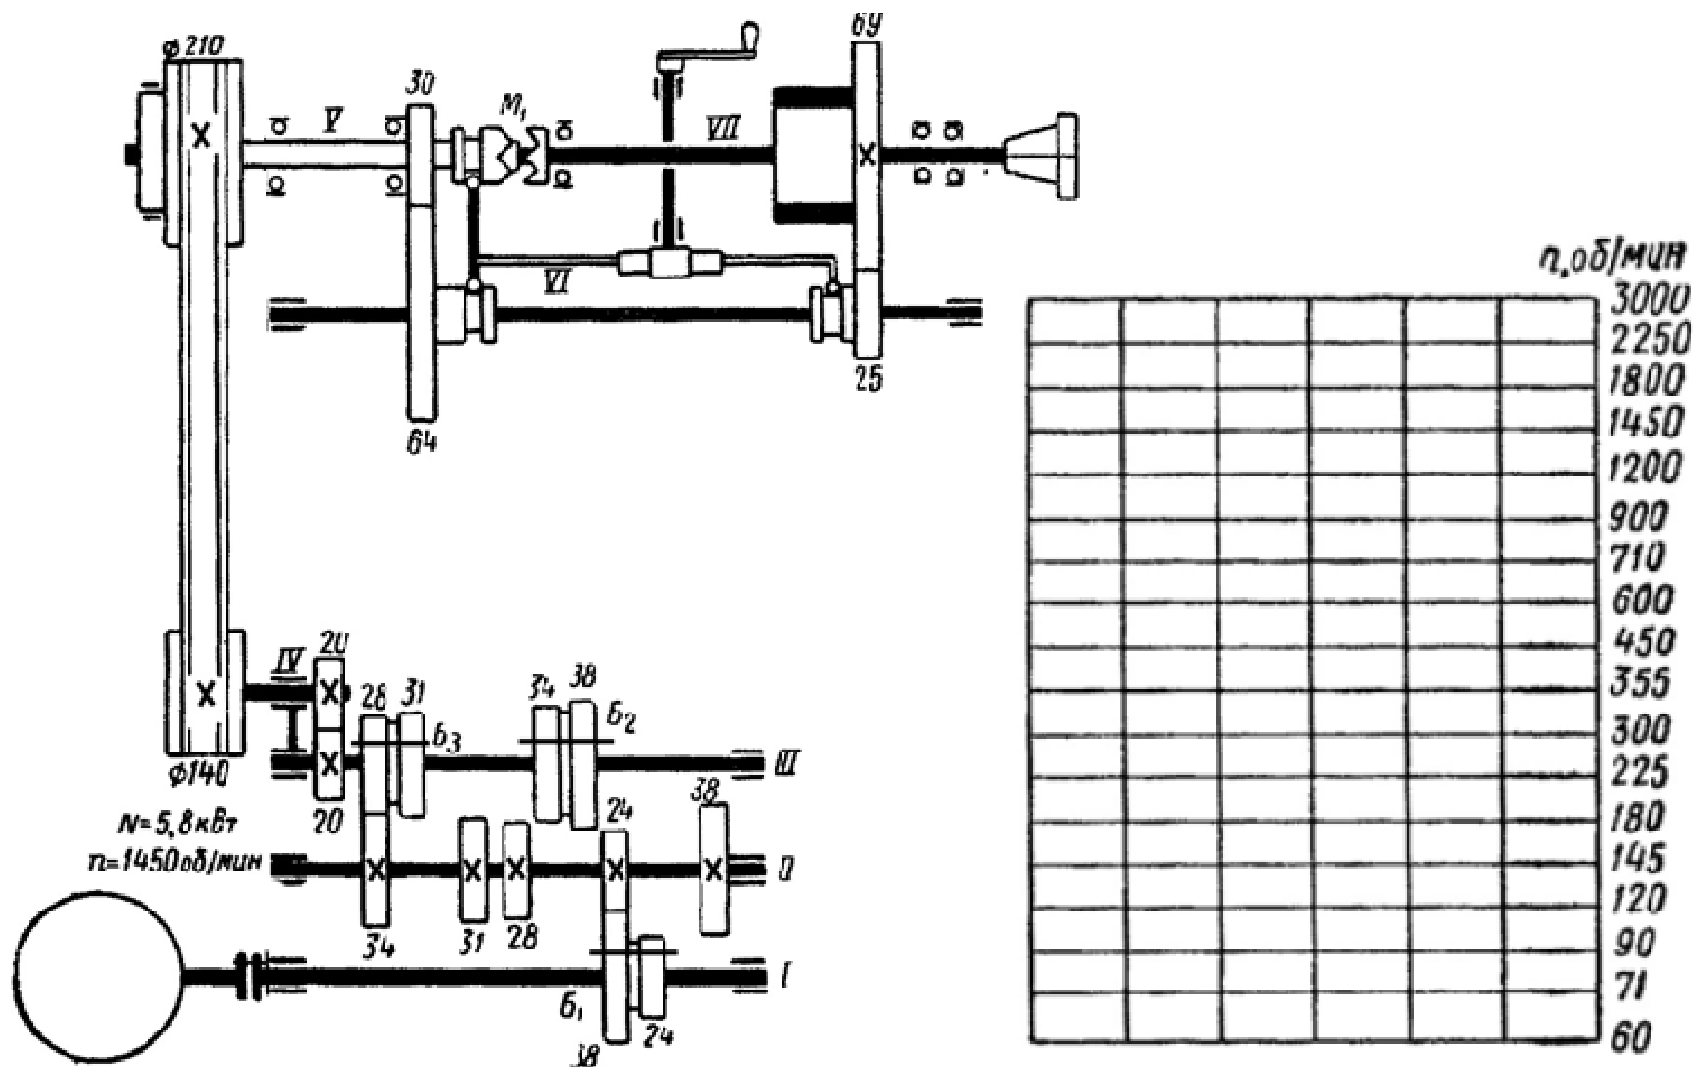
Типова коробка передач фрезерного верстата.
